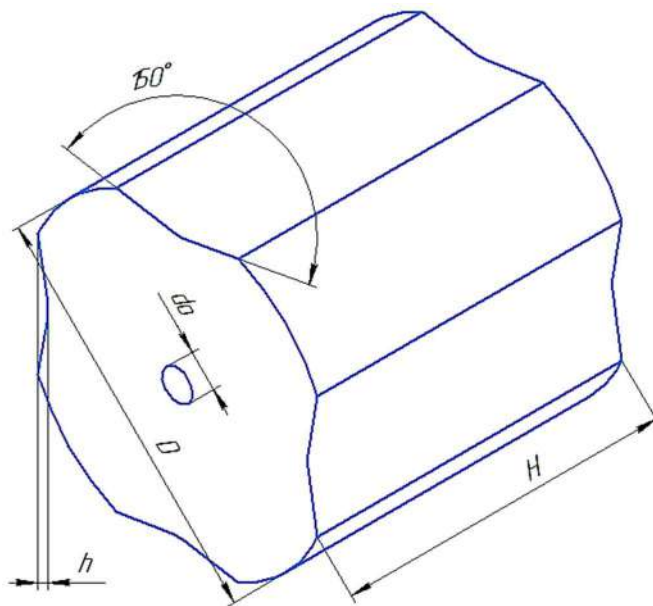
3D-модель профільованої заготовки на чотирипроменевий переріз
